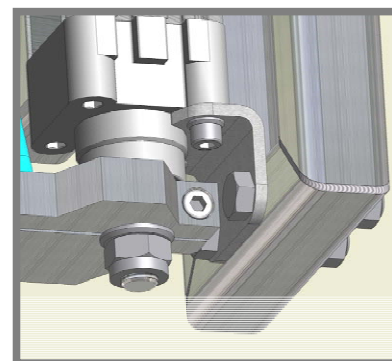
Detail uchycení pohonu řezací hlavy.
